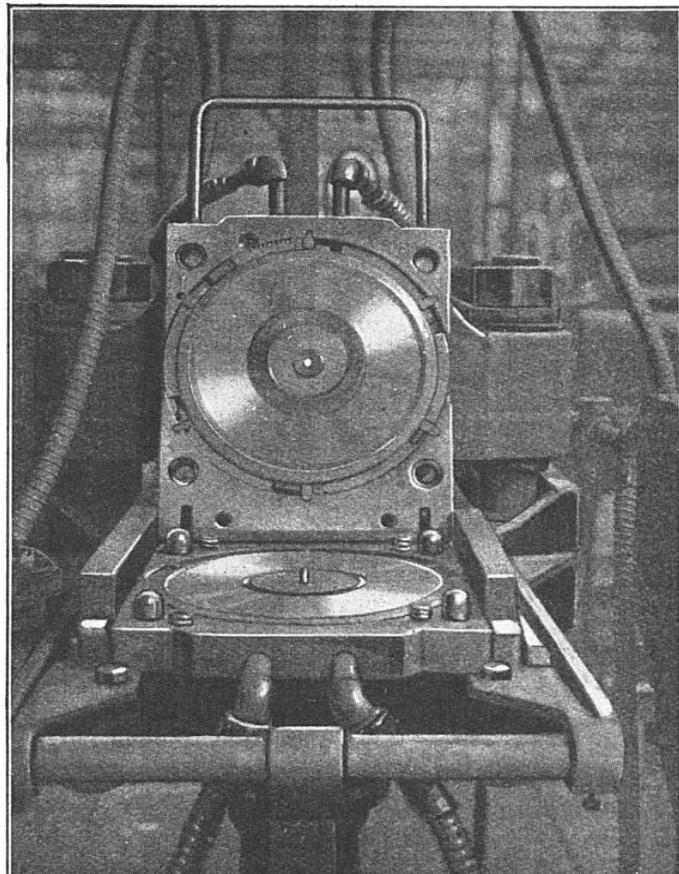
VUE DE FACE D'UNE PRESSE (OUVERTE) POUR LE TIRAGE DES DISQUES DÉFINITIFS DU COMMERCE
